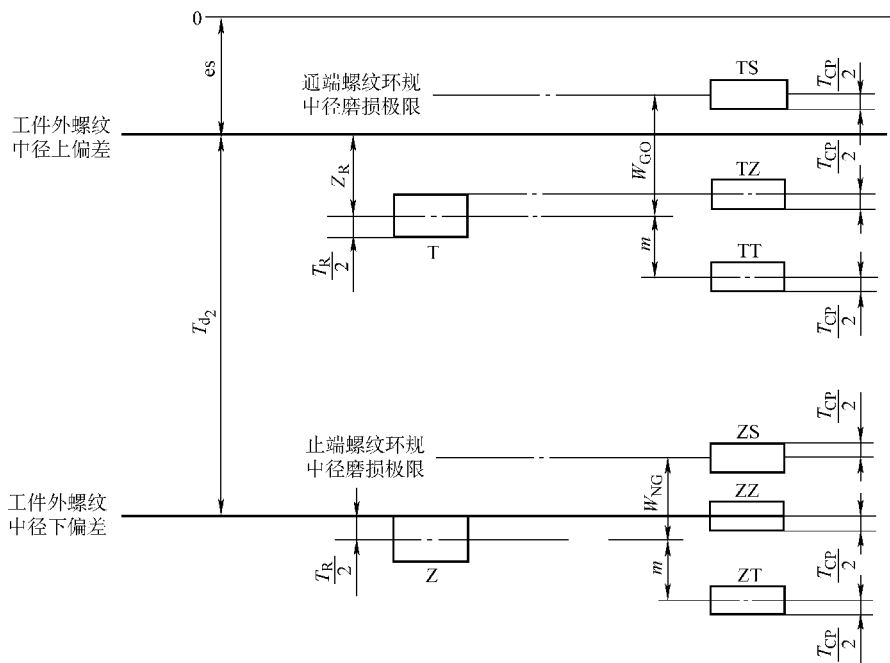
螺纹环规和校对螺纹塞规螺纹中径公差带
